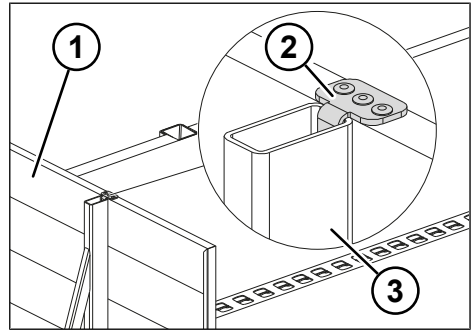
Mobile Stirnwand Befestigungshaken
